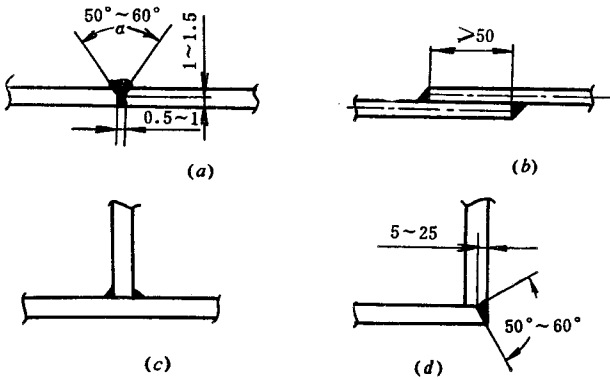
硬塑料板焊接的焊缝形式
